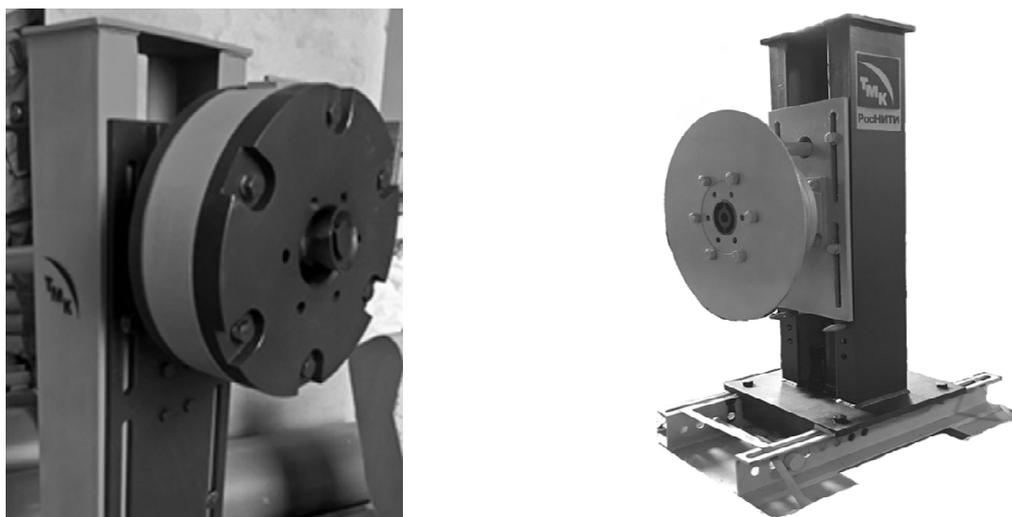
Примеры оборудования для нанесения СДМ на внутреннюю поверхность гильзы
